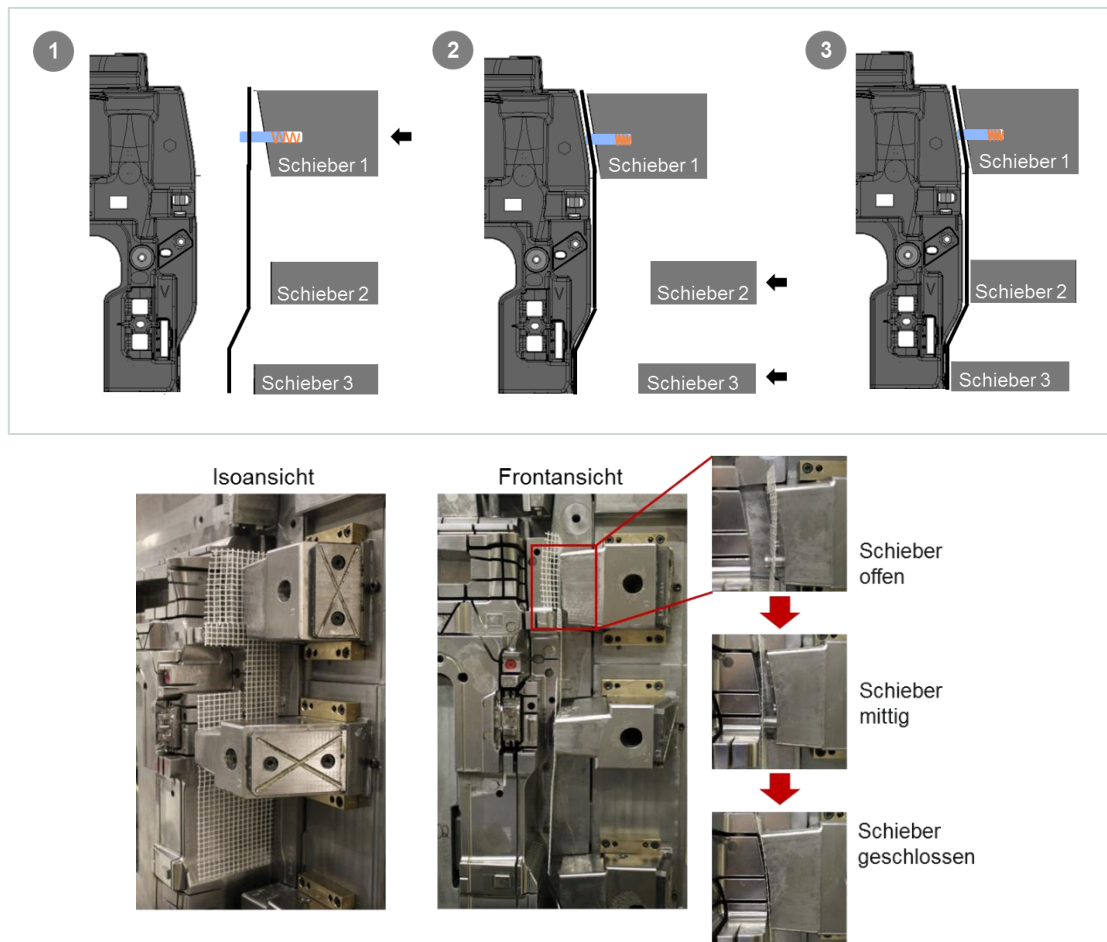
Positionierung der Fasereinleger im Spritzgusswerkzeug; schematische Darstellung (oben) und Detailaufnahme im Werkzeug (unten)
